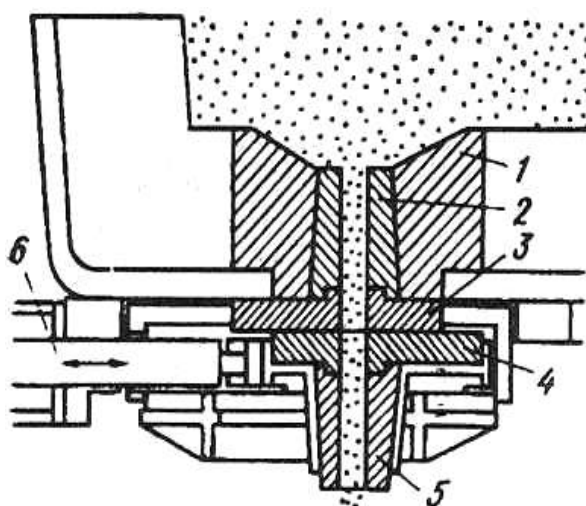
Схема шиберного затвора для бесстопорной разливки:
